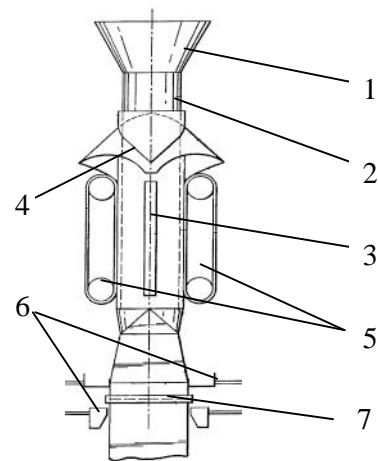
Компонування машини з механізмом формування внутрішніх складок пакету: 1 – приймальна воронка; 2 – рукавоутворювач; 3 – губка поздовжнього зварювання; 4 – формувальний ворот; 5 – механізм протягування плівки; 6 – механізм формування складки; 7 – губки поперечного зварювання
